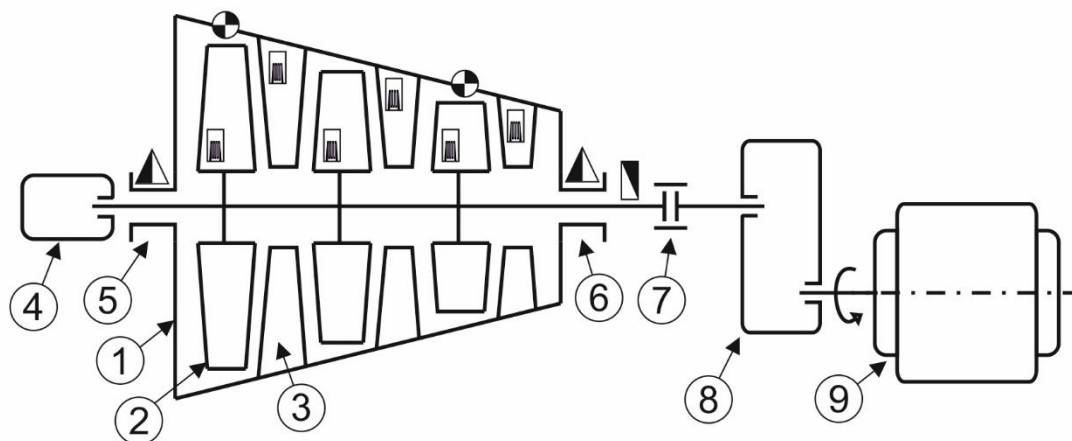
Схема трассировки измерительных каналов по ротору компрессора
